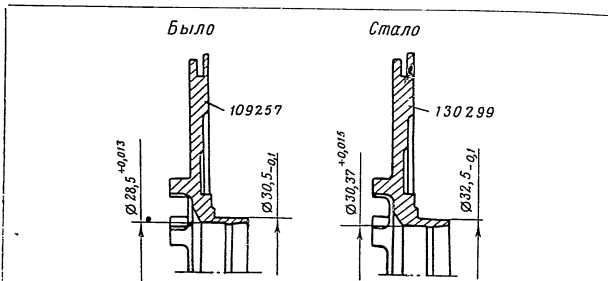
Зубчатое колесо верхнего запасного привода.
